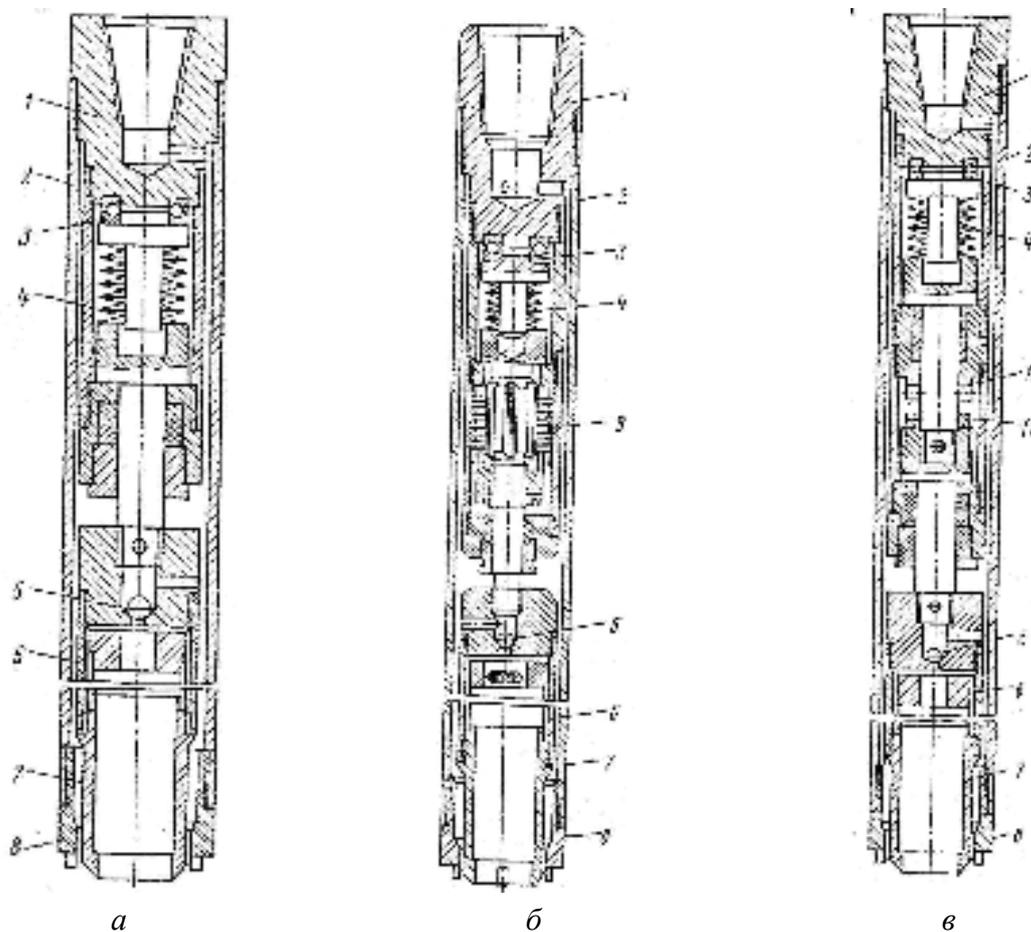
Двойной колонковый снаряд «Донбасс НИЛ»: *а* – «Донбасс НИЛ-1», *б* – «Донбасс НИЛ-2», *в* – «Донбасс НИЛ-3»: 1 – переходник; 2 – колонковая труба; 3 – упорный шариковый подшипник; 4 – тарельчатые пружины; 5 – шаровой клапан; 6 – керноприемная труба
